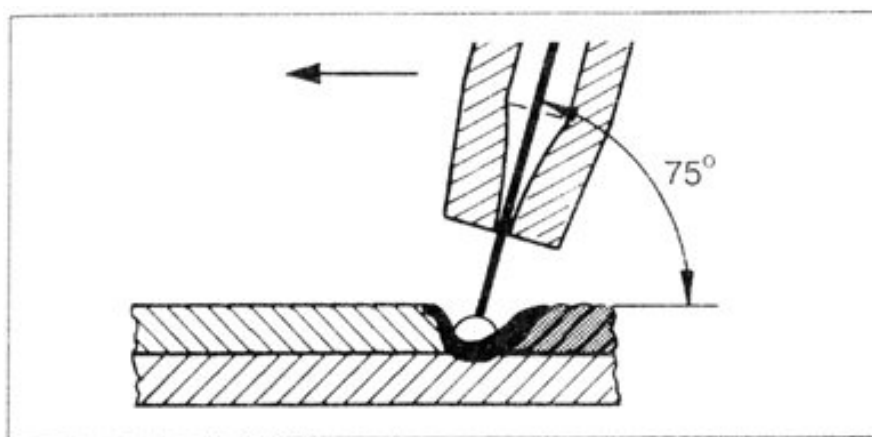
Положение горелки при сварке в среде защитного газа
